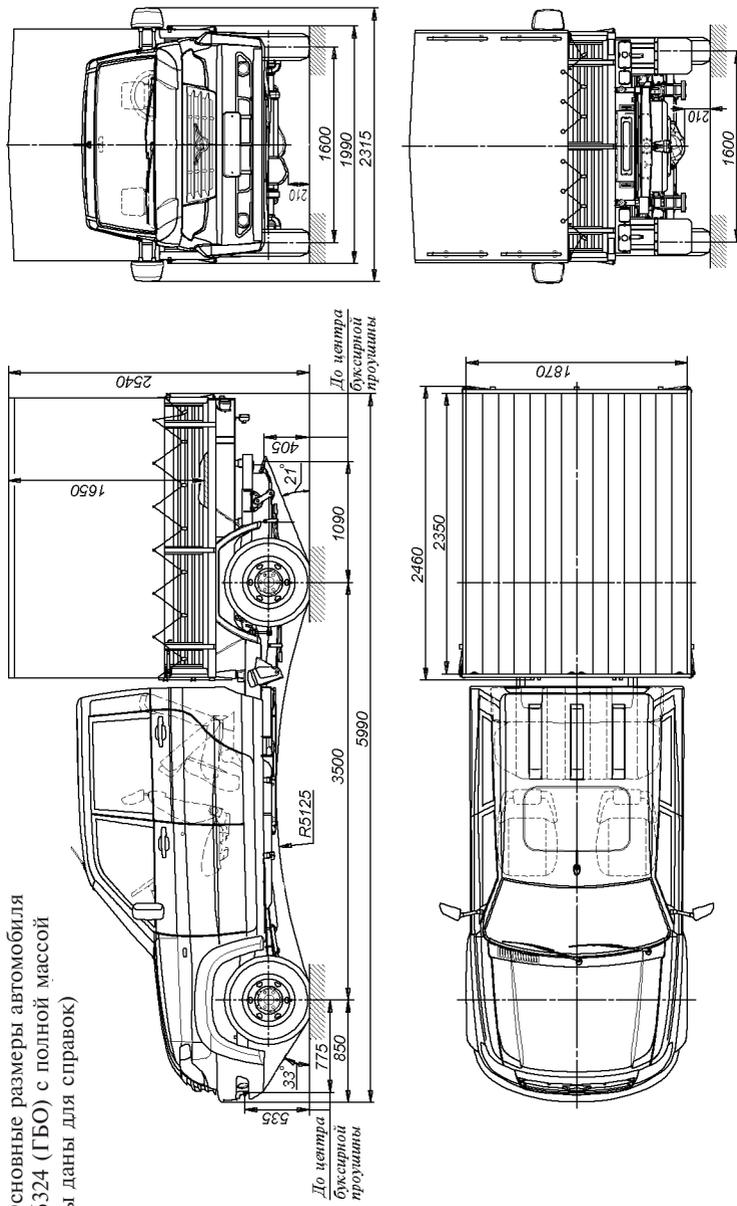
Основные размеры автомобиля УАЗ-236031 (ГБО) с полной массой (размеры даны для справок)
